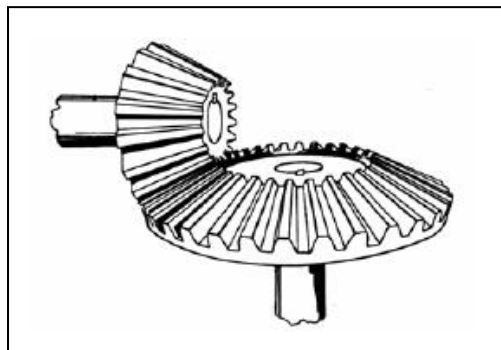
Engranajes Cónicos de Dientes Rectos⁶⁷
